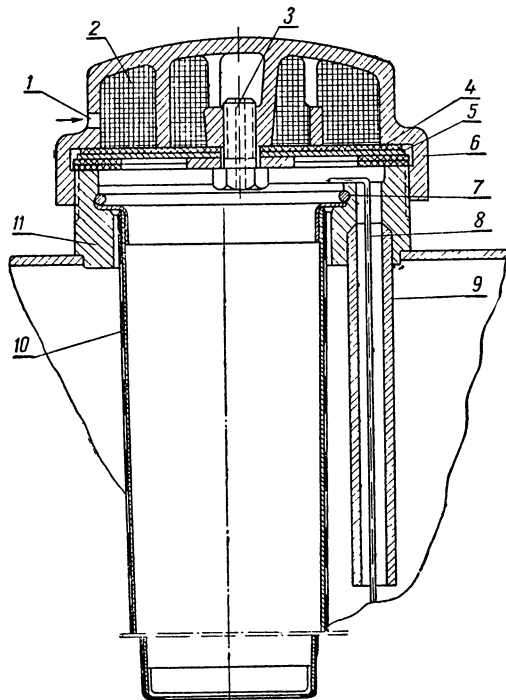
Горловина топливного бака и ее крышка: 1 — отверстие в крышке; 2 — набивка; 3 — болт; 4 — прокладка; 5 — шайба; 6 — крышка; 7 — пружинное кольцо; 8 — мерная линейка; 9 — трубка; 10 — сетчатый фильтр; 11 — горловина топливного бака
